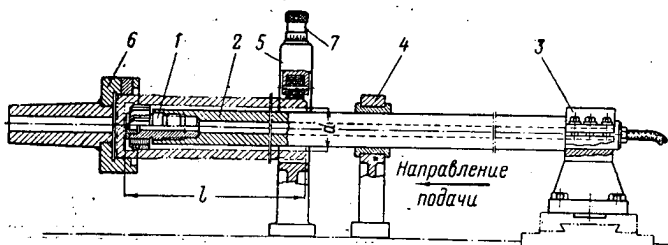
Схема наладки токарного станка для скоростного растачивания цилиндров.
